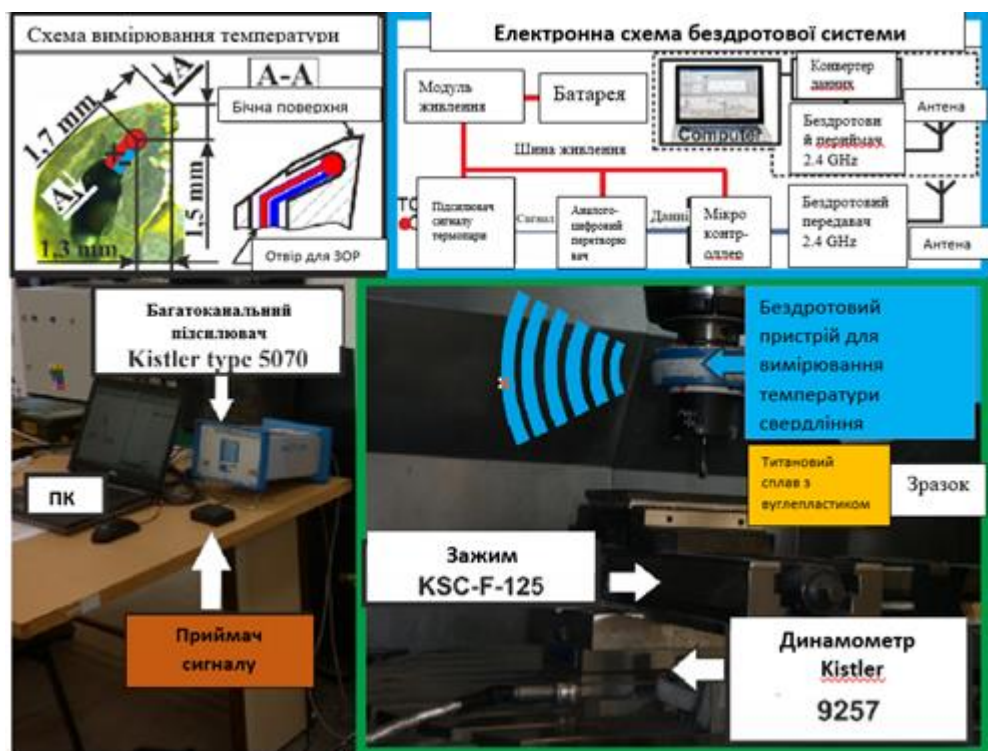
Експериментальна установка на базі фрезерного оброблювального центру DMU 85V
